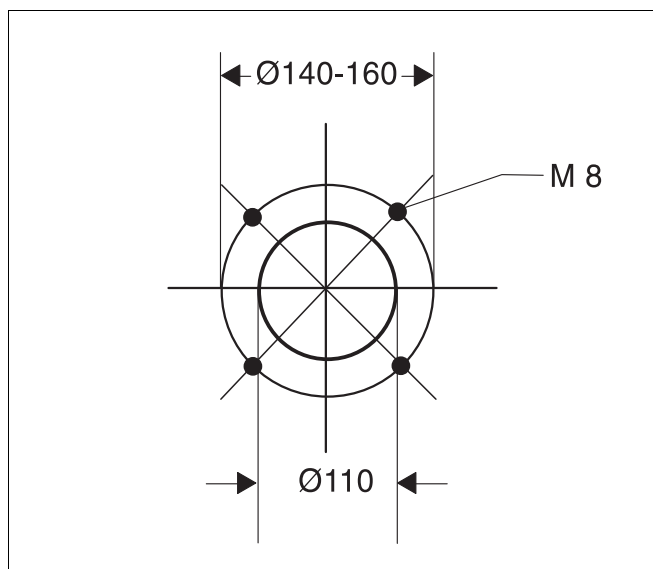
Anschlussflansch des Brenners (Maße in mm)
